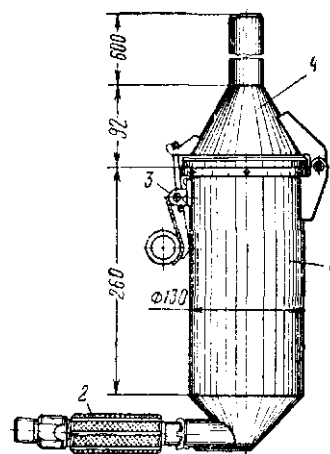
Пневмозабойник Конструкции ВНИИОМШСа
